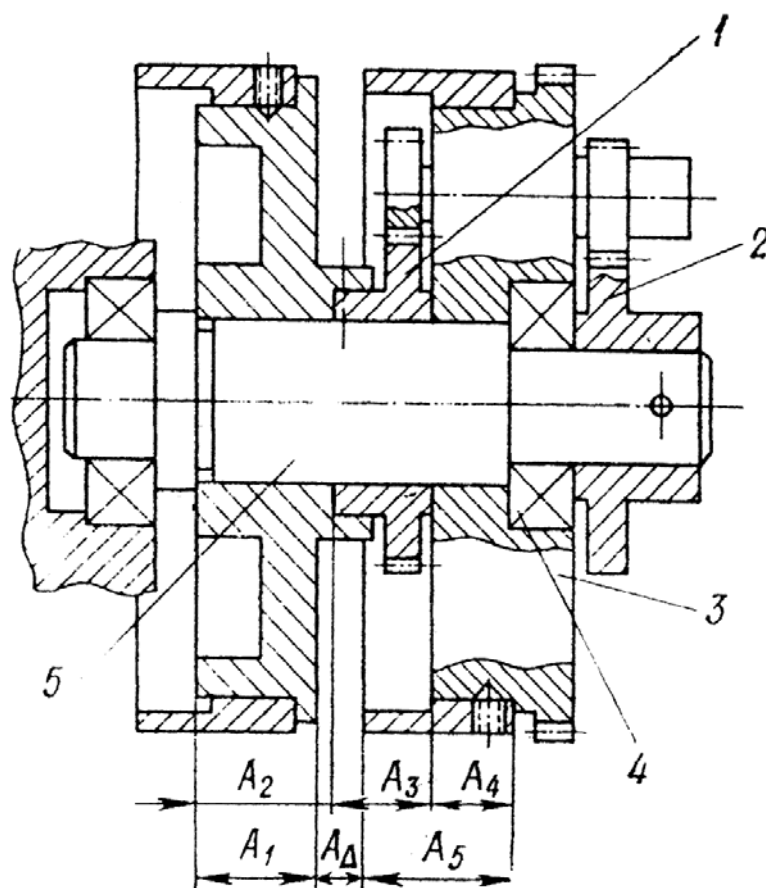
Узел подшипникового соединения: 1 – столик; 2 – колесо; 3 – водило; 4 – подшипник; 5 – вал
